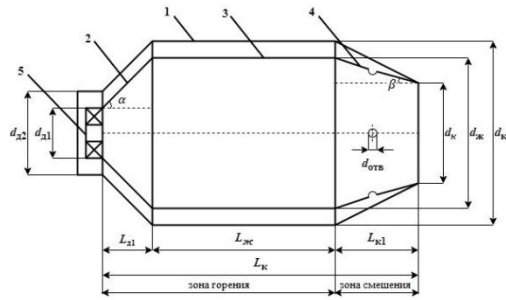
Основные габаритные размеры камеры сгорания: 1 – корпус; 2 – диффузор ЖТ; 3 – цилиндрическая часть ЖТ; 4 – газосборник; 5 – горелочное устройство.
